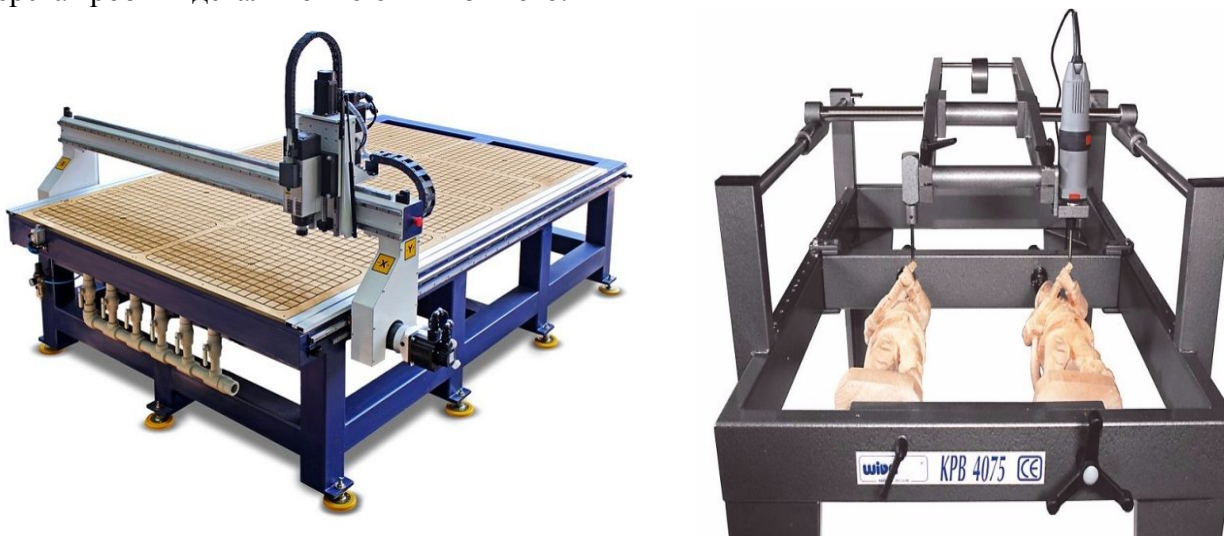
Промисловий та копіювально-фрезерний верстат по дереву з ЧПК
